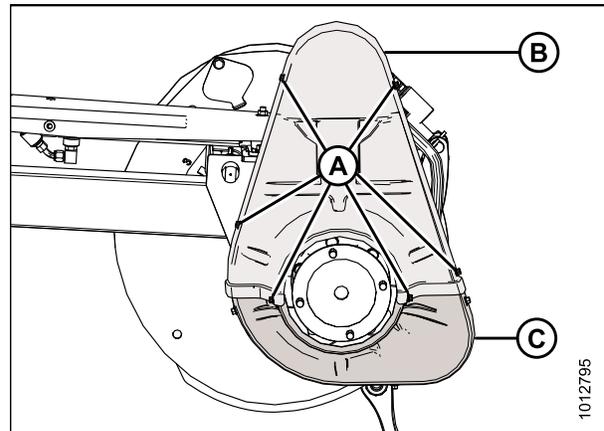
Крышка привода — сдвоенное мотовило
